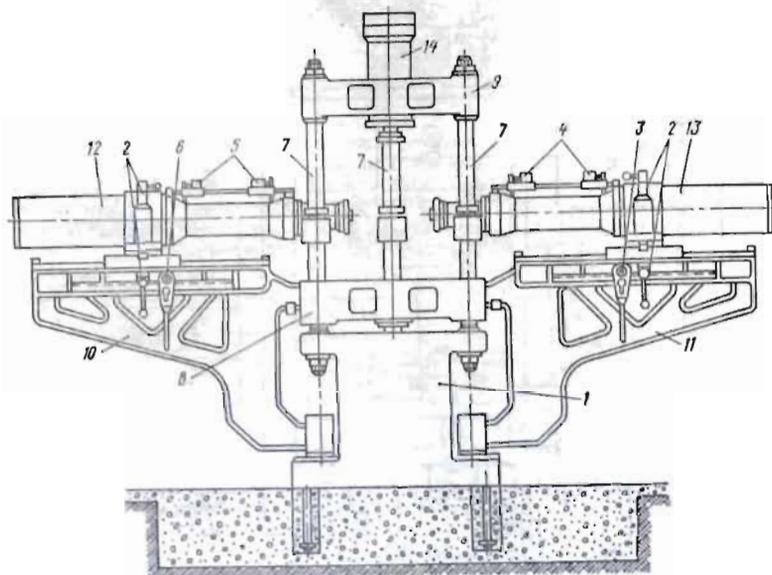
Гидравлический пресс формовки патрубков ПГФП-20/100
